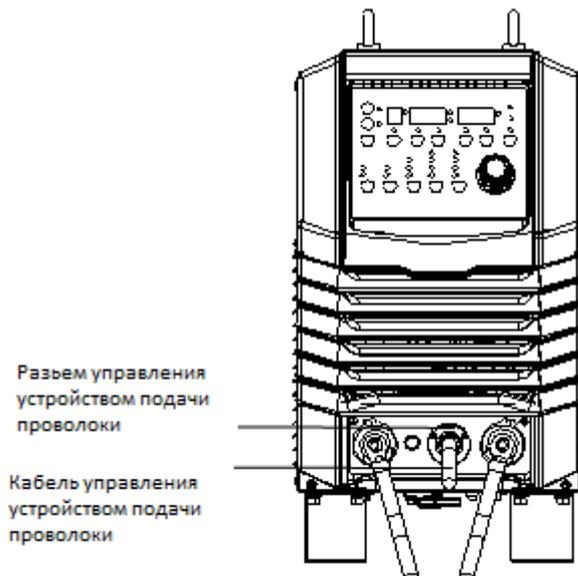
Схема подключения кабеля управления устройства подачи проволоки с разъемом сварочного аппарата.
